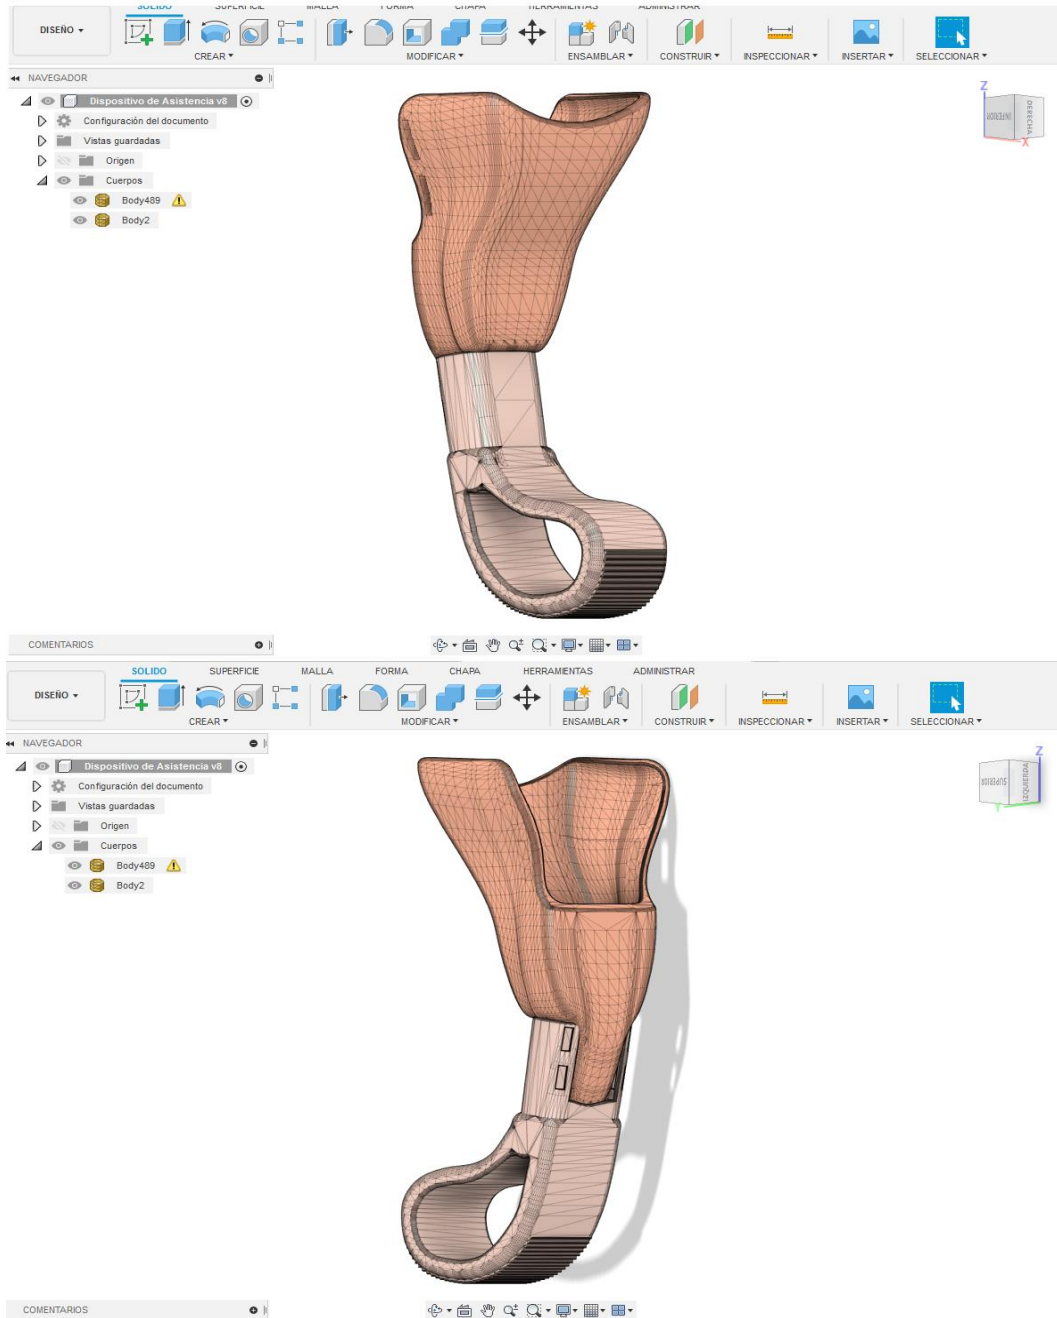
Diseño completo del prototipo de prótesis canina para extremidades delanteras Fuente: El Investigador
